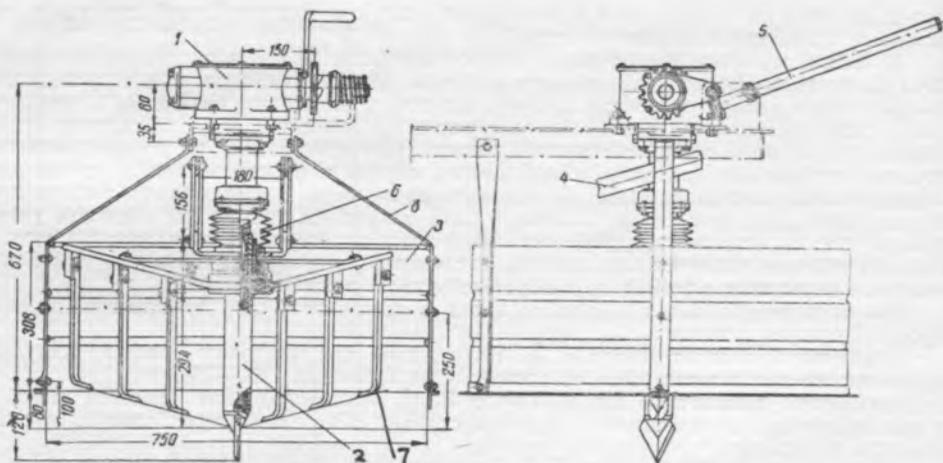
Редуктор к почвенной фрезе: 1 — редуктор; 2 — фреза; 3 — кожух фрезы; 4 — механизм подачи; 5 — рычаг выключения редуктора; 6 — защитный кожух от пыли; 7 — взаимозаменяемые ножи фрезы; 8 — планка кожуха
